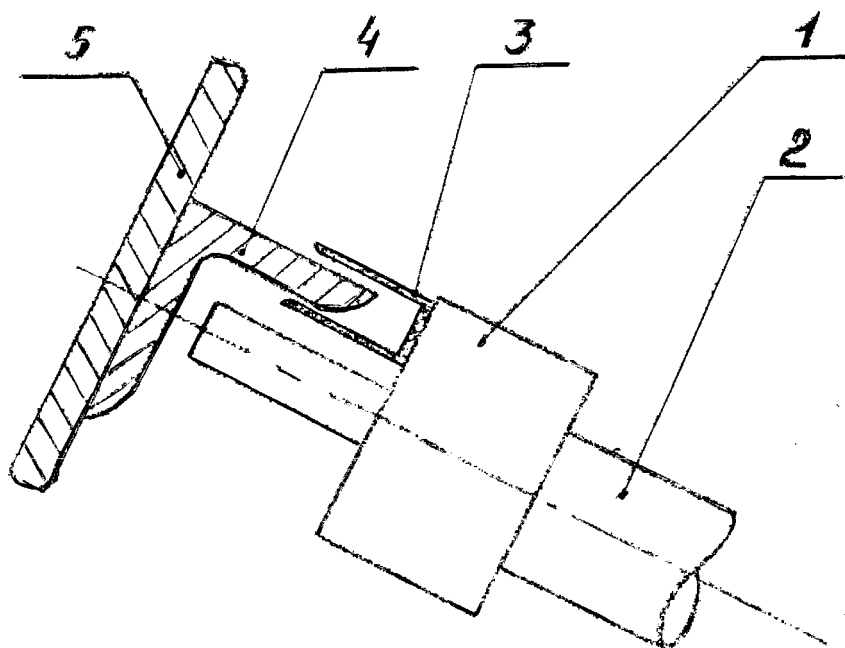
Схема обеспечения перемычки от края отверстия до края детали в ДАРМ-КС: 1 — рабочая головка импульсного клепального автомата; 2 — позиционер; 3 — щуп-вилка; 4 — профиль; 5 — обшивка
